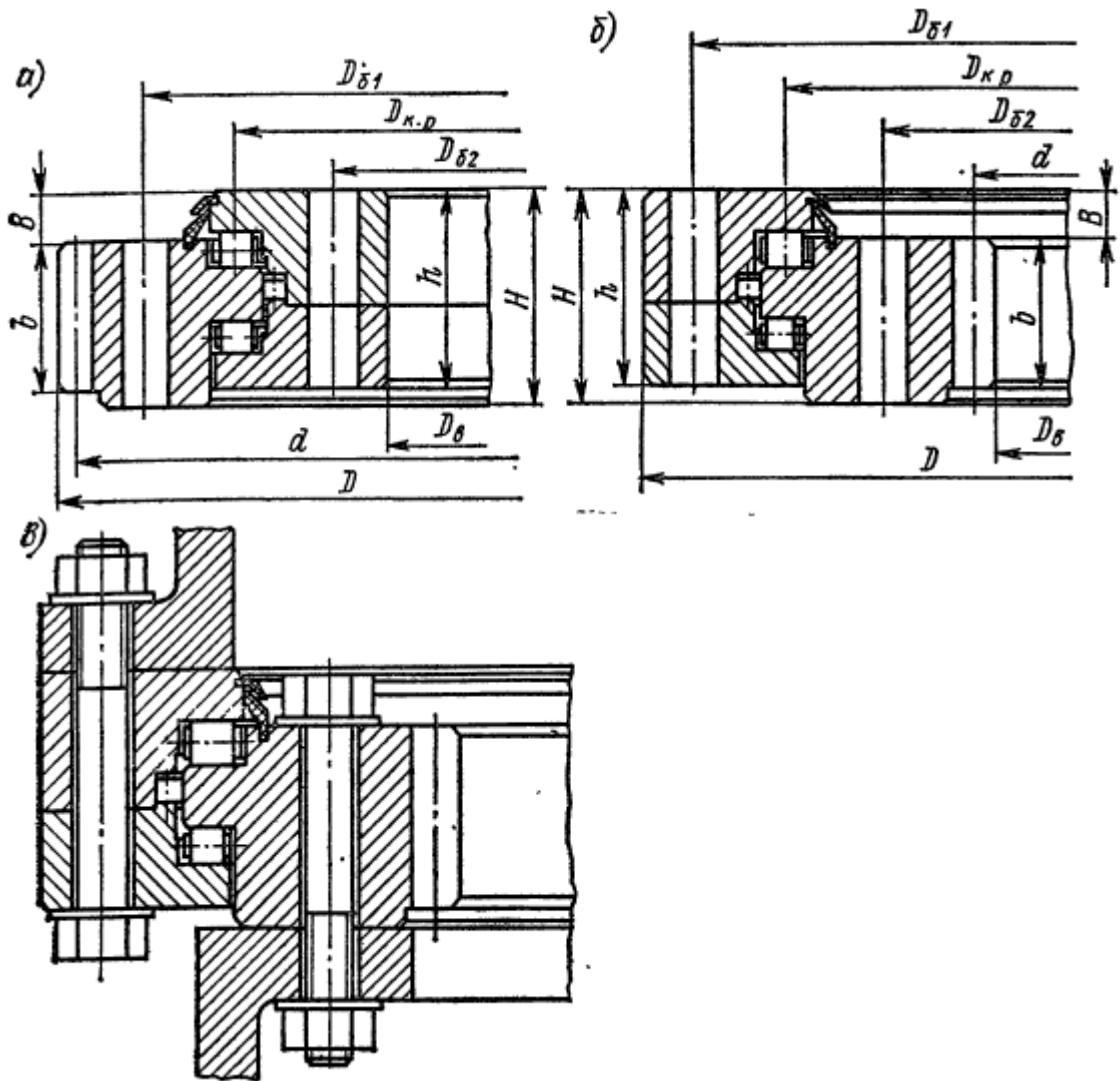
ОПК: а - однорядні роликові з зубами внутрішнього зачеплення; б - дворядні кулькові з зубами зовнішнього зачеплення
